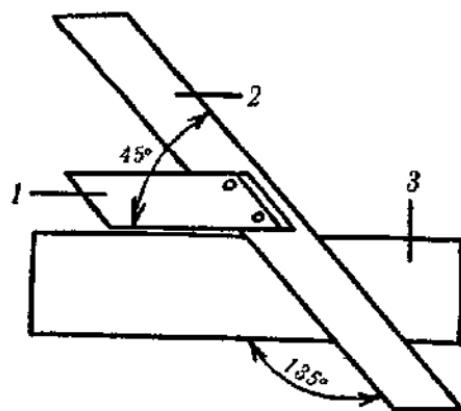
Ярунок: 1 — колодка (основание); 2 — линейка; 3 — размечаемая деталь.
